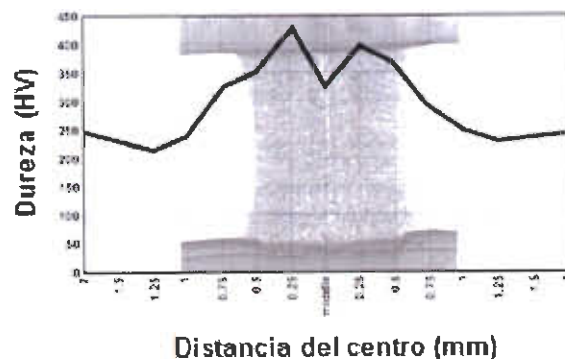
Dureza en Soldaduras HF de Aceros DP 280/600 ^[34]
